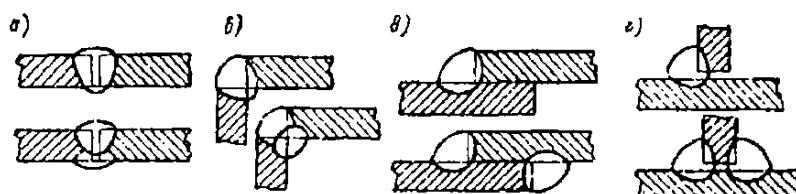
3 - Сварные соединения листовых конструкций:
